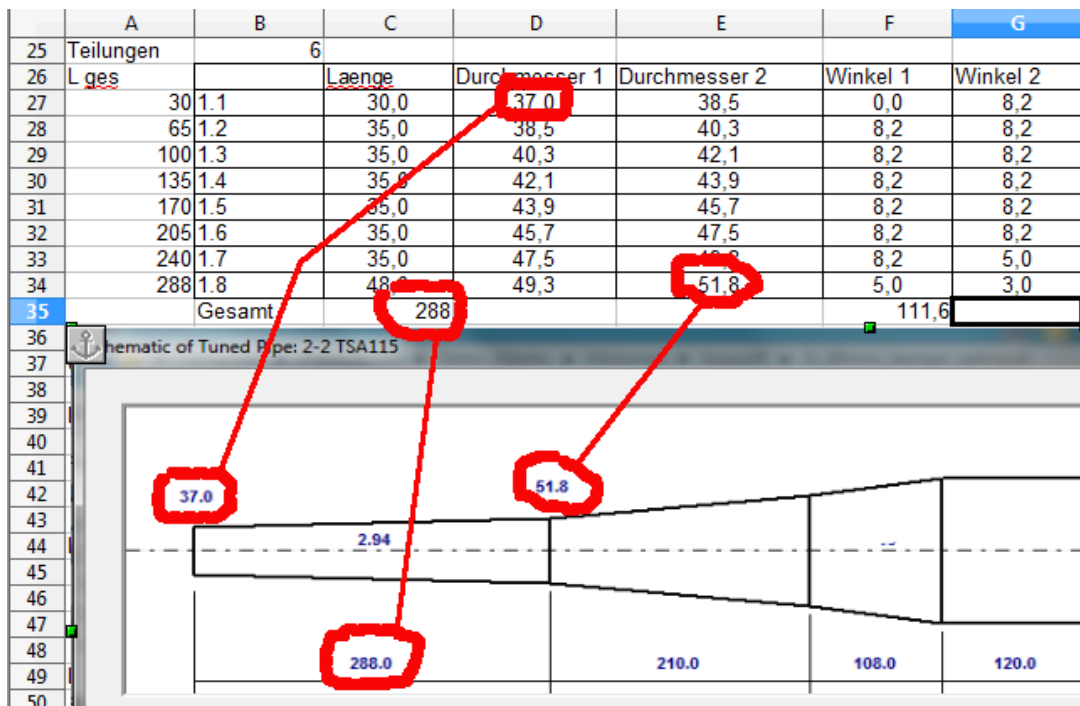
Layout-Tabelle zur Ermittlung der Einzel-Konen.
